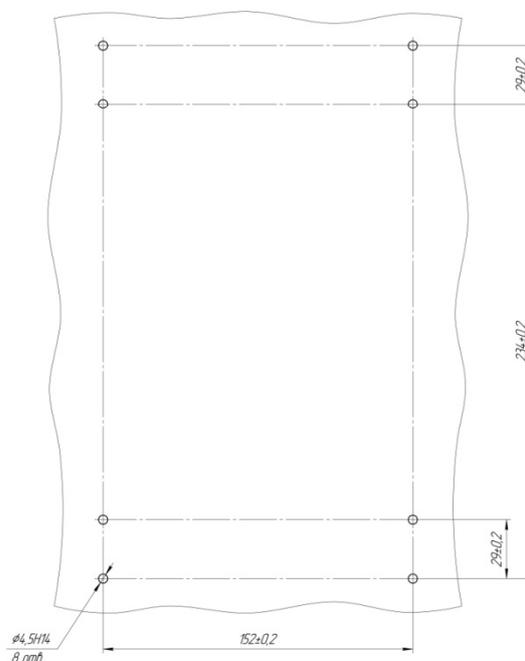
Габаритные и присоединительные размеры устройства PC83-BC при внешнем монтаже, обеспечивающем его поворот влево/вправо
